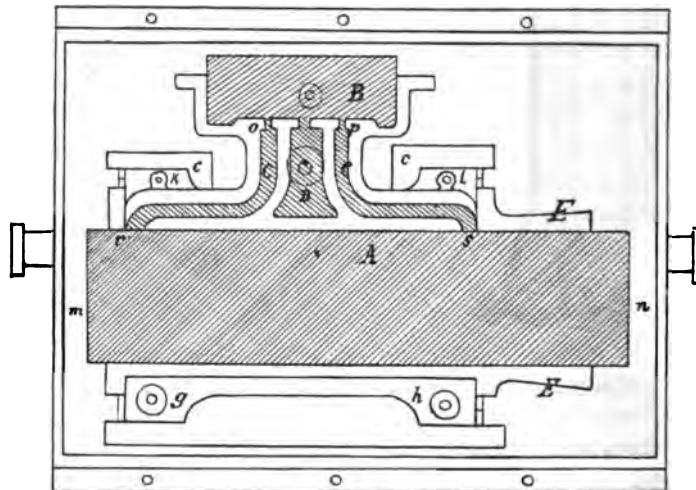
Grundriss des unteren Formkastens mit eingelegten Kernen.
